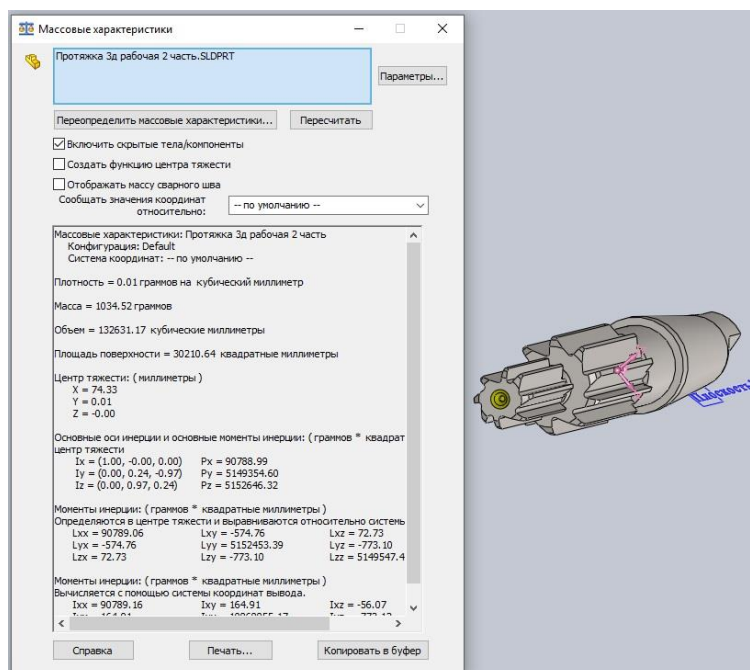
Маса готового інструменту (зварна заготовка)
